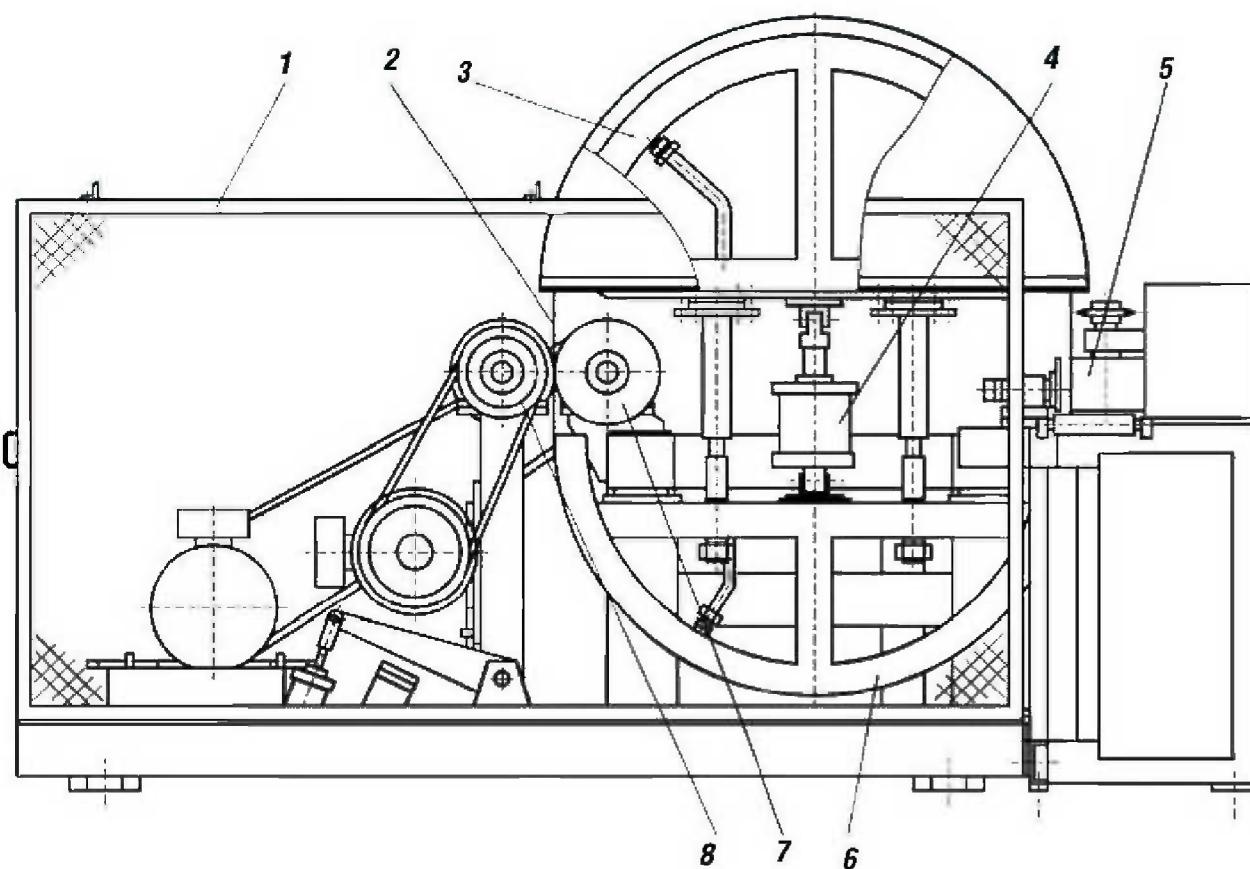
Конструкция ленточнопильного станка с пилой, движущейся по криволинейным аэростатическим направляющим:
